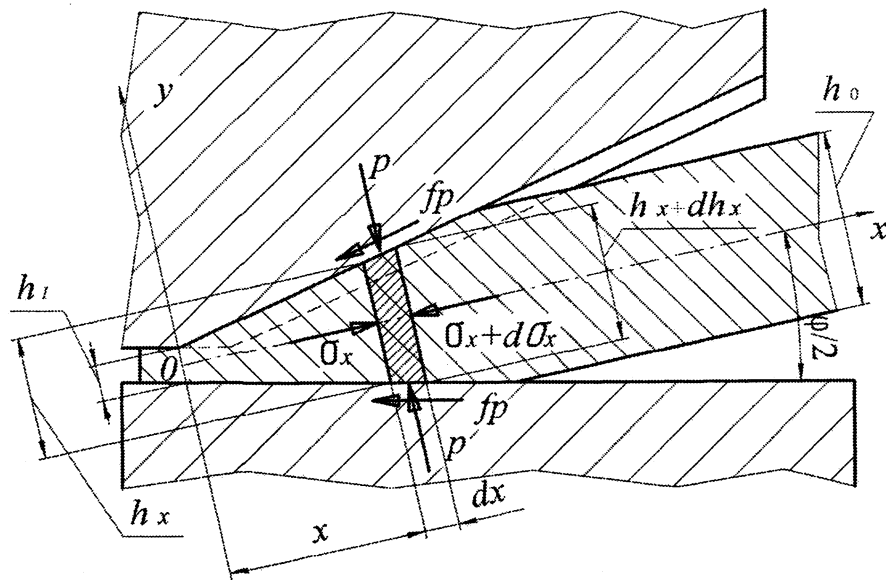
Схема формообразования рельефа при свободном повороте заготовки
